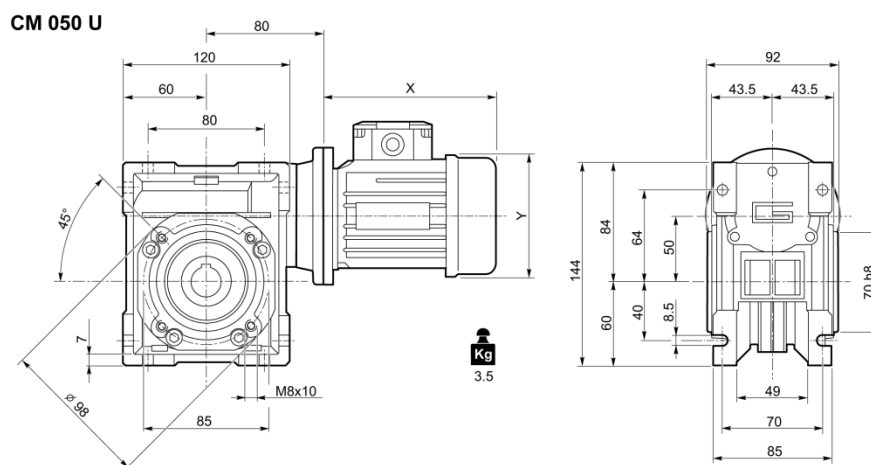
Rozměrová tabulka vybraného motoru [20]
